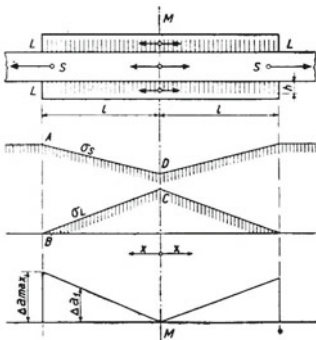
Stab mit durch Flankennähte aufgeschweißten Laschen. Das Blech ist voll.
